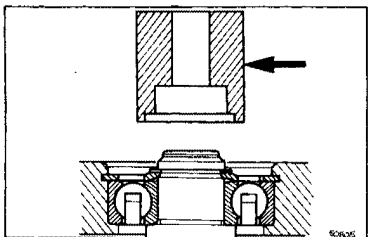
Установка пружинного кольца вторичного вала специальным приспособлением
